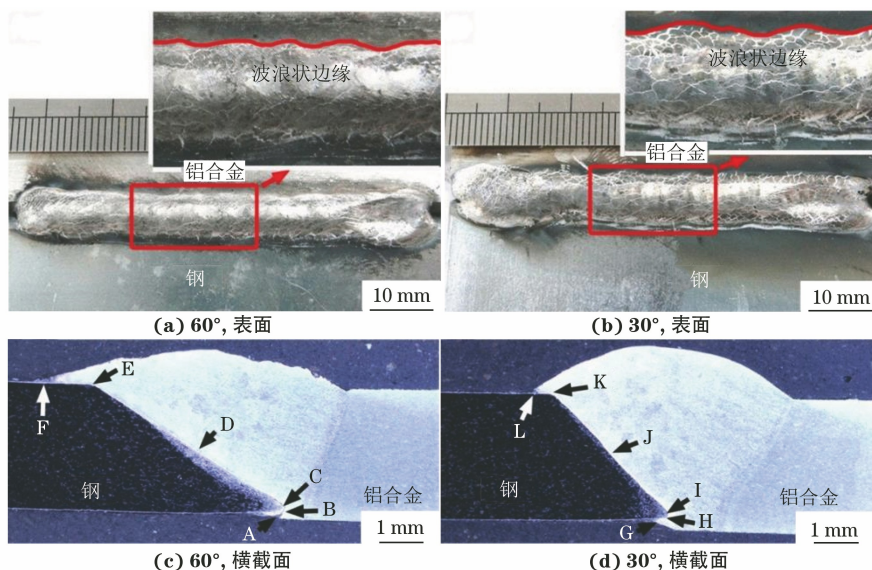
不同坡口面角度钢板/铝合金板焊接接头焊缝表面和横截面宏观形貌
